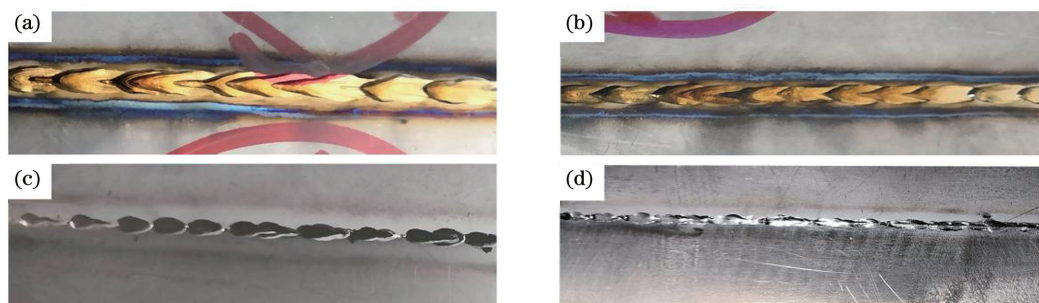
不同激光功率下焊缝宏观形貌。(a)1.3 kW, 焊缝正面;(b)1.3 kW, 焊缝背面;(c)1.5 kW, 焊缝正面;(d)1.5 kW, 焊缝背面
